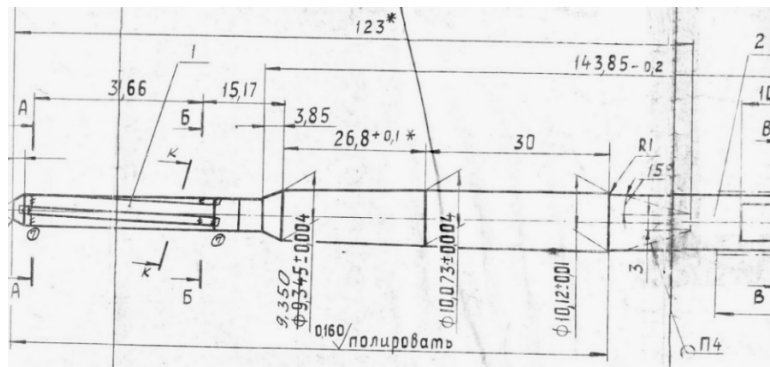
Креслення інструменту з твердого сплаву ВК20 для виготовлення стволів вогнепальної зброї шляхом радіального обтиснення трубчастої заготовки ствола довгомірну конічну заготовку з твердого сплаву, який отримували методом рідкофазного спікання порошкових брикетів. При цьому заготовки отримували з підвищеним припуском на механічну обробку (шліфування) через викривлення зразків при спіканні. Крім того, після шліфування заготовки та отримання деталі з остаточними розмірами на поверхні робочої частини інструменту іноді були великі пори, що навіть за наявності однієї пори не дозволяло використовувати дорогий і трудомісткий інструмент для роботи. Тому на прохання підприємства нами була зроблена спроба отримання довгомірних заготовок з твердого сплаву ВК20 шляхом ударного видавлювання у відповідний приймач. При цьому передбачалося одержання заготовок двох видів – ступінчастої та конічної, у яких припуск на механічну обробку заготовки було мінімізовано. Проведені дослідження з ударного видавлювання твердого сплаву дозволили встановити умови (температурно-часовий та енергетичний режими), за яких вдавалося отримати повноцінну довгомірну заготовку. Вигляд довгомірних заготовок двох типів, які отримані за різних умов ударного видавлювання, представлено на рис. 6.3.
